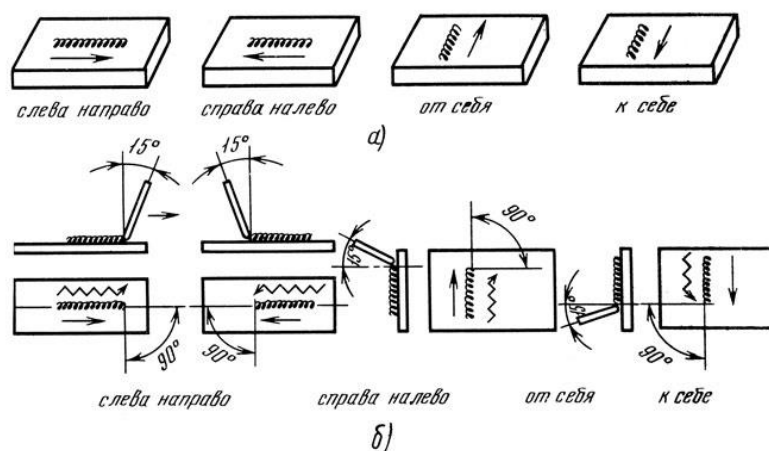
Направления сварки (а) и наклон электрода (б)
